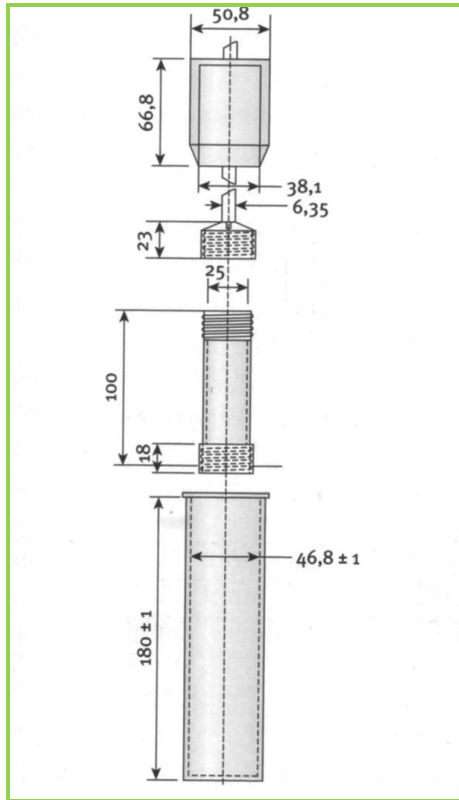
Appareil 3, à piston (dimensions en millimètres)
